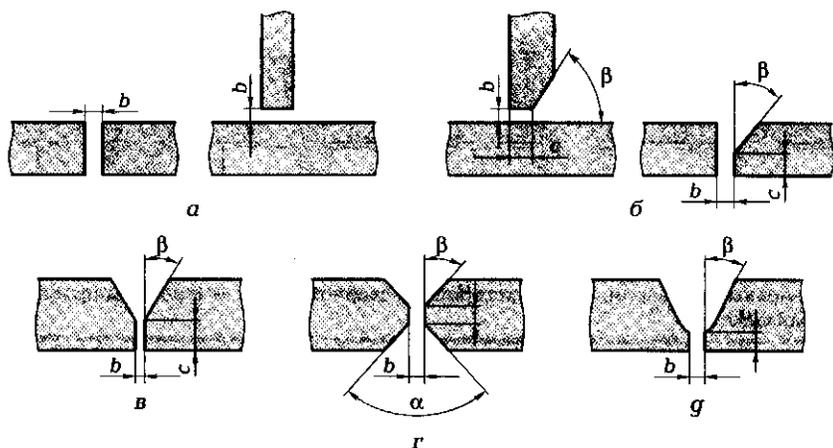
Конструктивные элементы разделки кромок под сварку:
